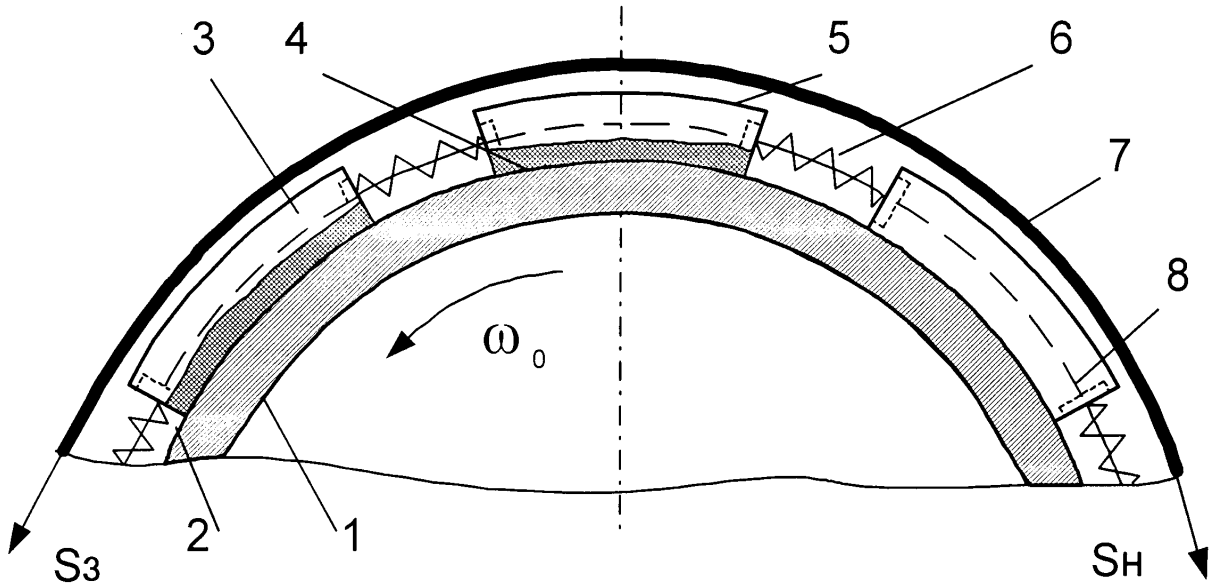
Схема стрічково-колодкового гальма з рухомими фрикційними накладками: 1, 2 – гальмівний шків і його робоча поверхня; 3, 4, 5 – фрикційна накладка з внутрішньою та зовнішньою поверхнями; 6 – циліндрична пружина; 7 – гальмівна стрічка з робочою поверхнею; 8 – циліндричні стрижні
